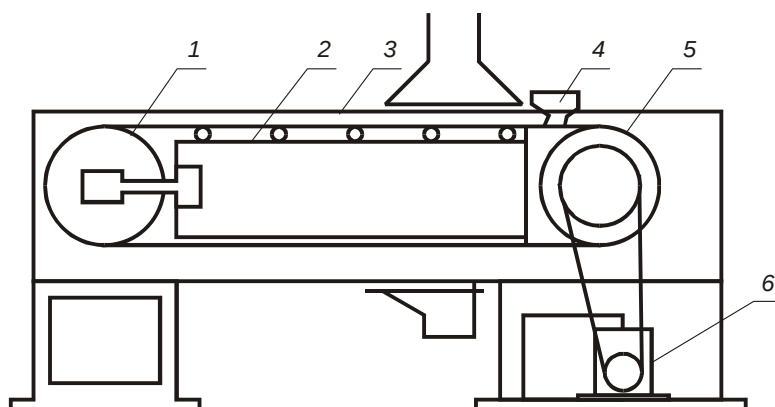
Установка для изготовления пиротехнических пленок методом отлива из раствора: 1, 5 — барабаны; 2 — рама; 3 — медная лента; 4 — фильера; 6 — электропривод
